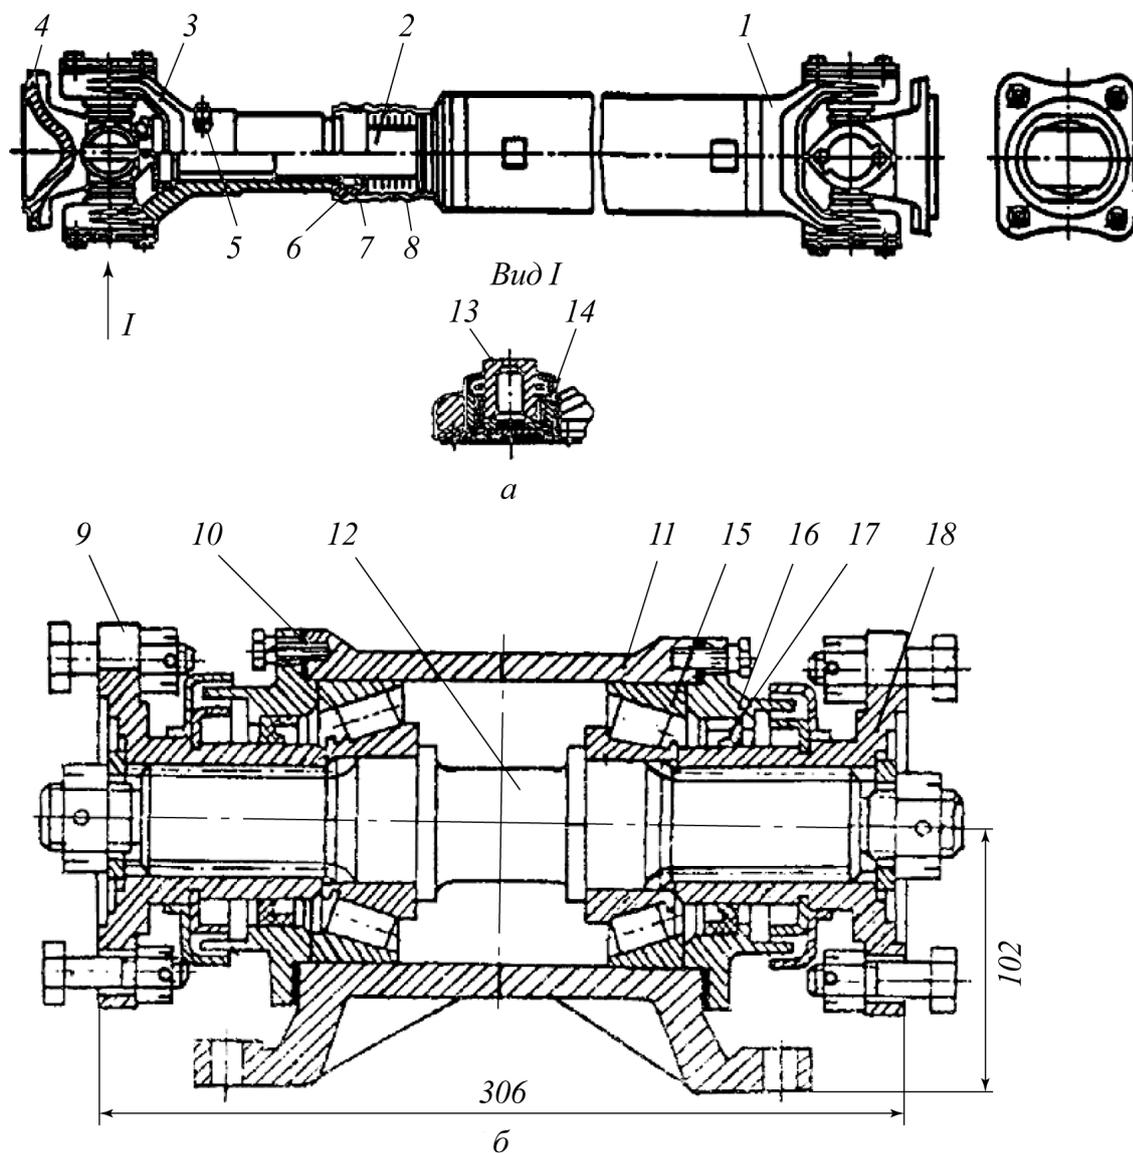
Карданный вал и промежуточная опора: а – вал; б – опора: 1 – труба; 2 – втулка шлицевая; 3, 4 – вилка шарнира; 5 – пресс-масленка; 6 – крышка прижимная; 7 – сальник войлочный; 8 – чехол резиновый защитный; 9, 18 – фланец; 10, 16 – крышка; 11 – корпус; 12 – вал промежуточной опоры; 13 – крестовина; 14 – подшипник игольчатый; 15 – подшипник конический; 17 – манжета
